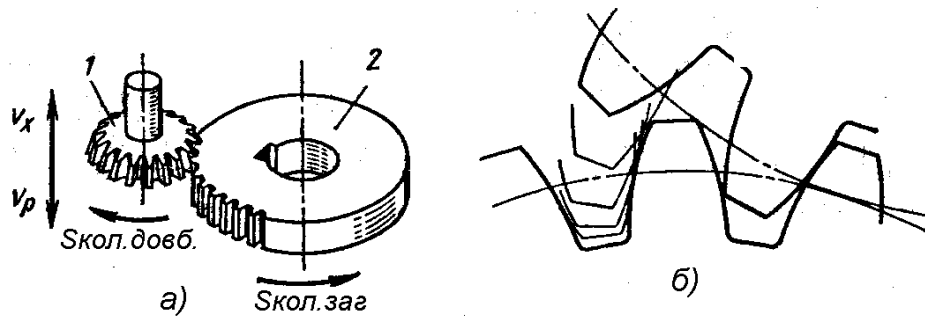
Схема формоутворення зубців циліндричного колеса
